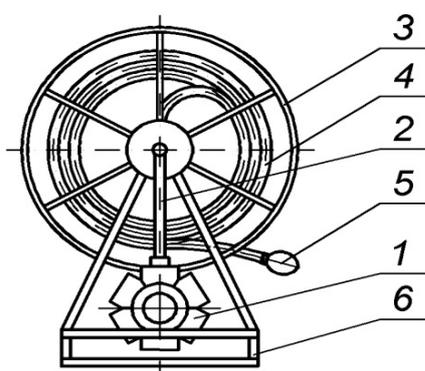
Схема устройства промывки дренажа: 1 – насос; 2 – трубопровод; 3 – барабан; 4 – промывочный рукав; 5 – промывочная насадка; 6 – рама
